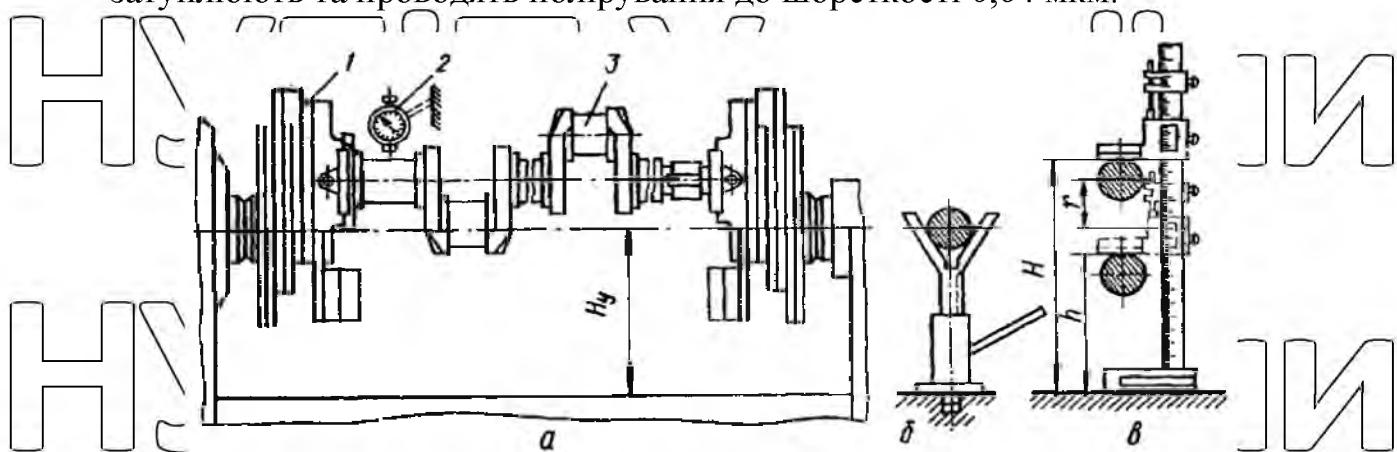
Схема установки колінчастого вала на верстаті обробки
